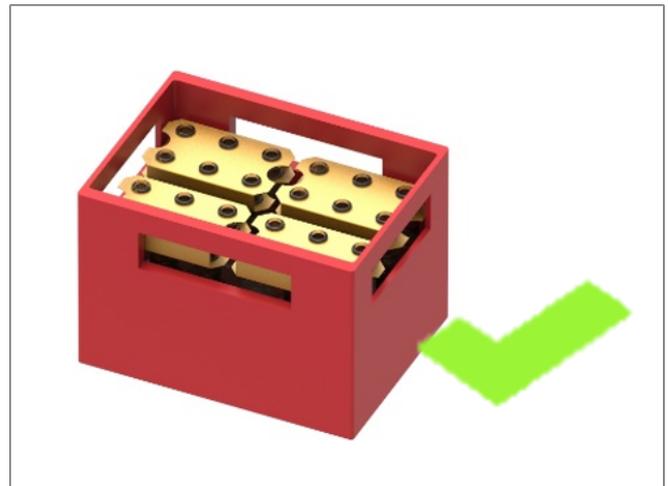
Günstige Anordnung von Multipacks im Kasten
